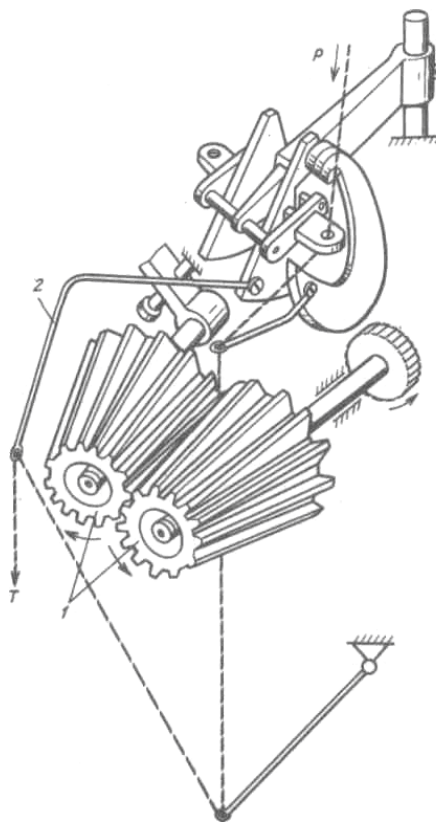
Механизм подачи нити с зубчатыми колесами
